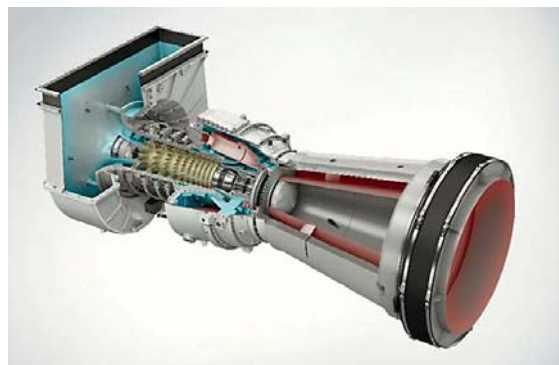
Газотурбинный двигатель SGT-100 (вырез четверти)
